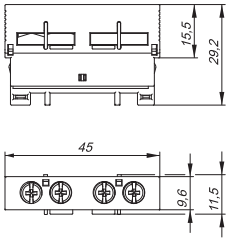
Габаритные и установочные размеры оболочки защитной / Figure 2 – Overall and mounting
